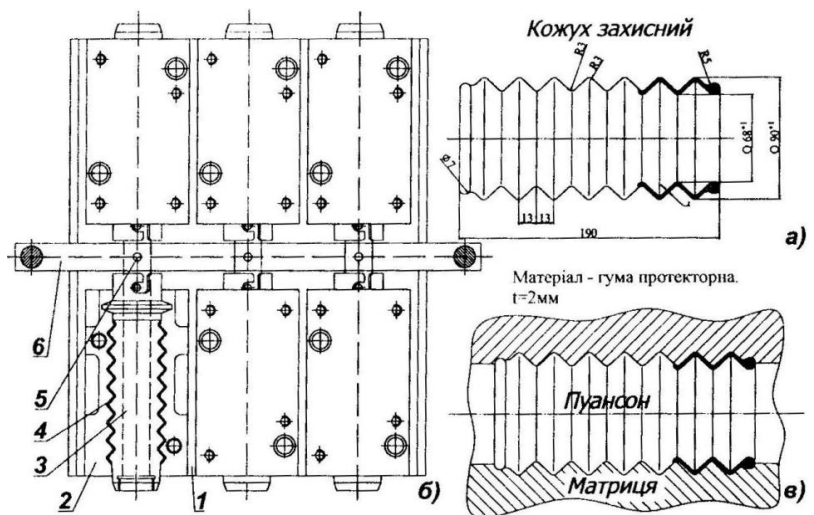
Пресформа шестимісна для виготовлення кожуха захисного
